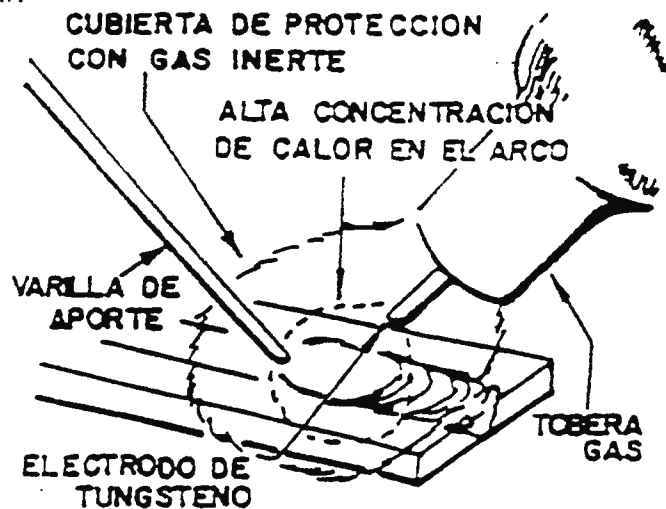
Forma de operar con proceso de soldadura T.I.G.
